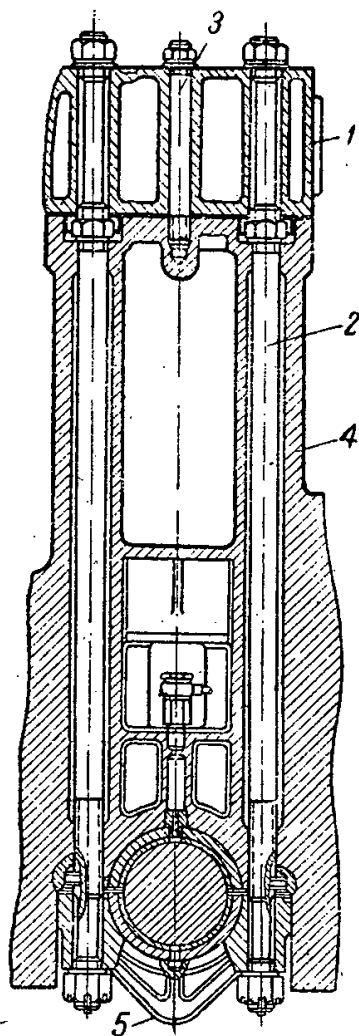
Крепление головок цилиндров и крышек коренных подшипников:
